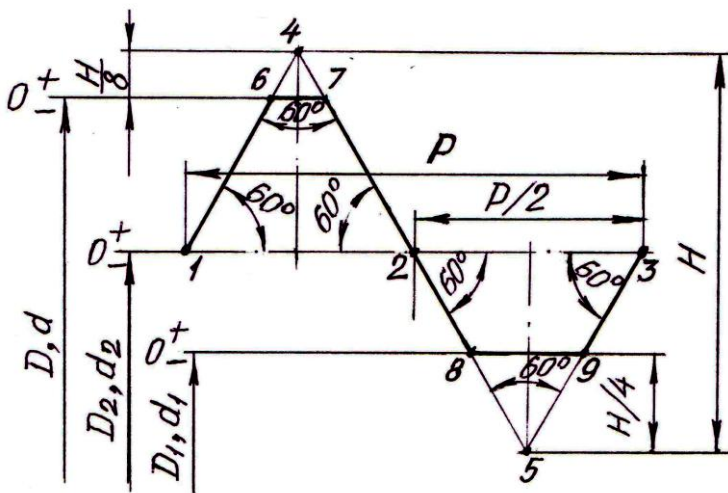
Побудова схеми розміщення полів допусків різьбового з'єднання
